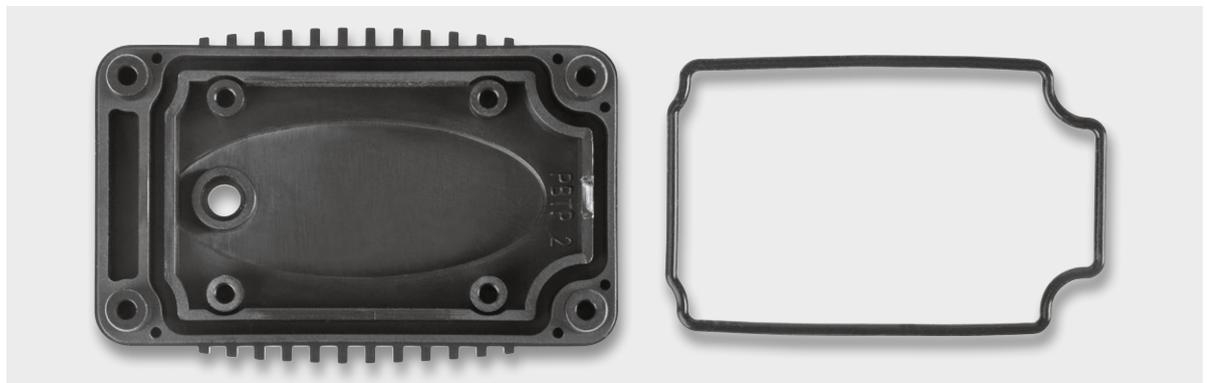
Montage der Gummidichtung im Gehäusedeckel
